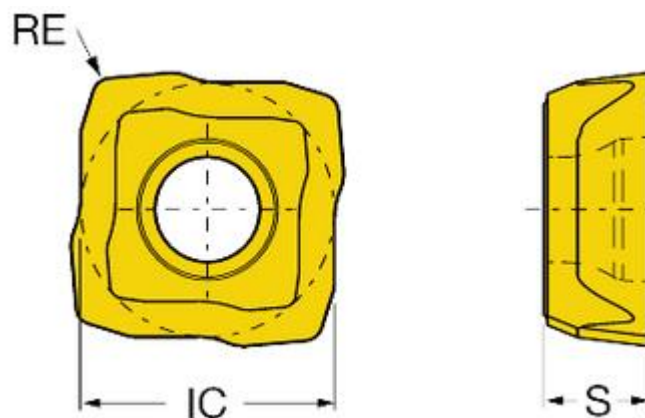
Пластинка ріжуча 880-06 04 06H-C-GR
